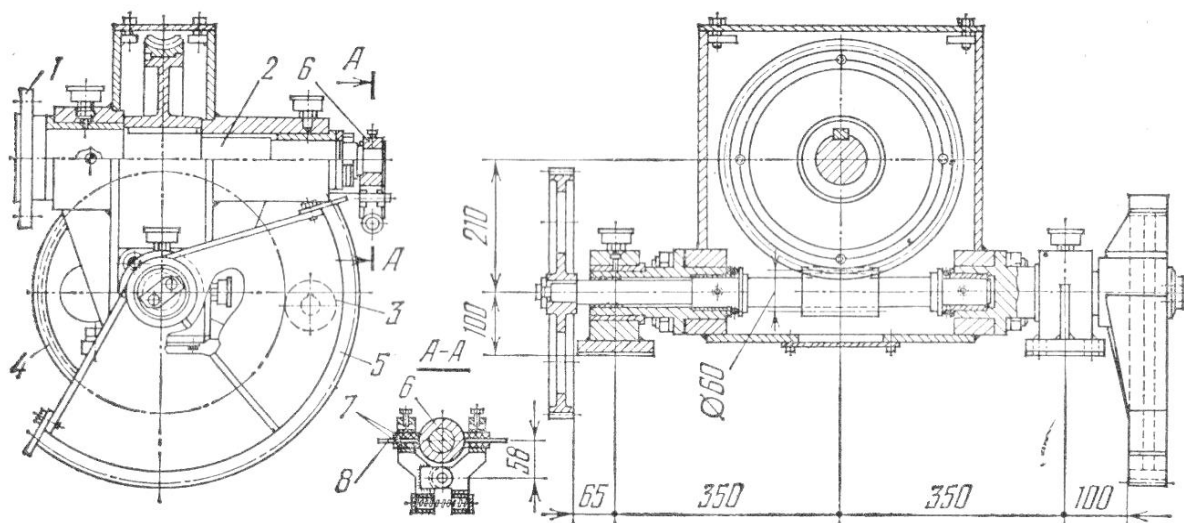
Привод манипулятора Т – 25М: 1 – фланец для крепления планшайбы; 2 – шпиндель; 3 – ведущая сменная шестерня редуктора; 4 – ведомая сменная шестерня; 5 – зубчатый сектор механизма наклона планшайбы; 6 – бронзовое кольцо токосъемника; 7 – медно – сетчатые щетки токосъемника; 8 – наконечник провода
